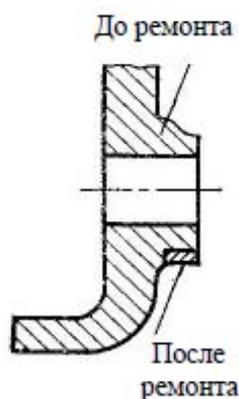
Схема установки бандажей для восстановления обломанной бобышки корпусной детали
